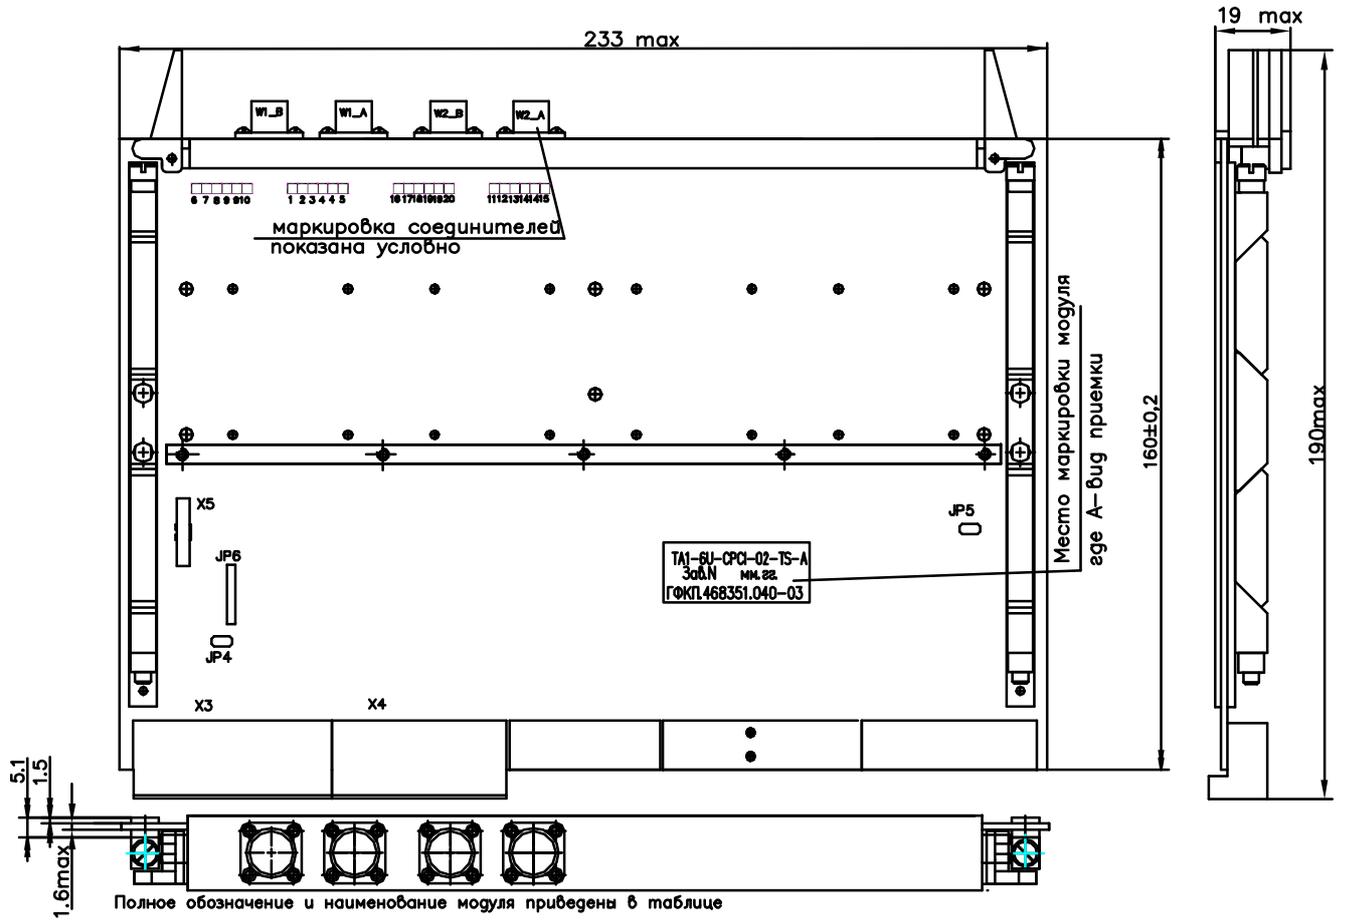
Габаритный чертеж изделия TA1-6U-CPPI-02-TS-A с кондуктивным теплосъемом и выходными разъемами RJ45
